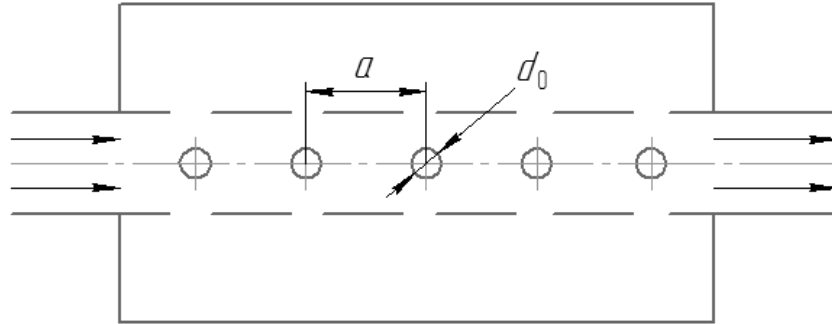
Однокамерний концентричний резонаторний глушник
